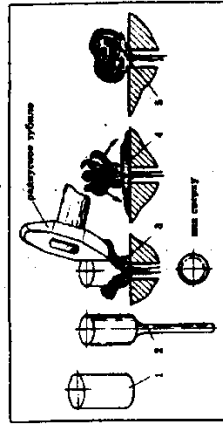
Изготовление целькованной розы: 1 — заготовка; 2 — отламыва стержня; 3 — надрубка лепестков; 4 — расковка лепестков и их формирование; 5 — сформированный цветок
